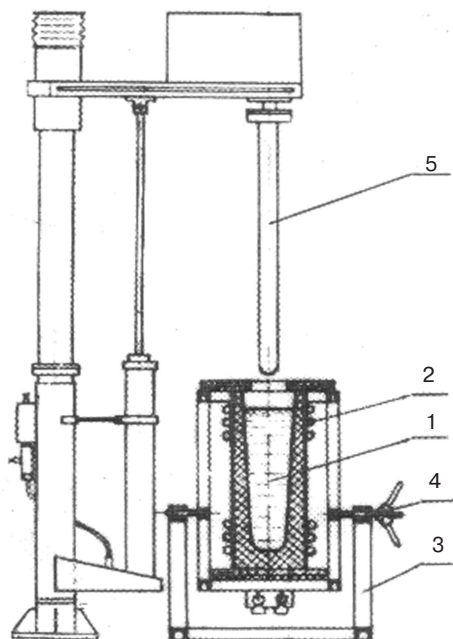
Схема установки для намораживания ферросилида (~14 % Si) на стальную трубу: 1 – расплав; 2 – индуктор; 3 – стойка; 4 – поворотный механизм; 5 – труба кристаллизатора
